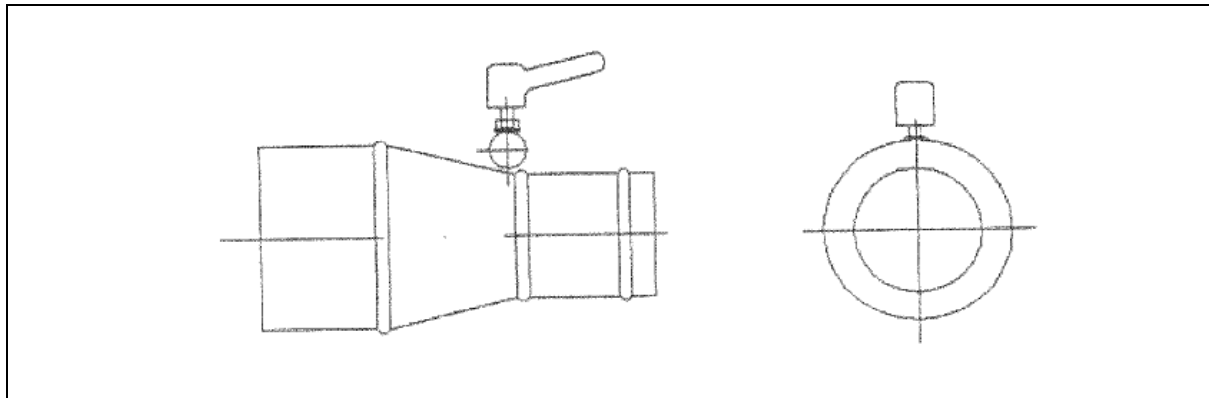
Darstellung Blechtülle rund mit Klemmschraube
